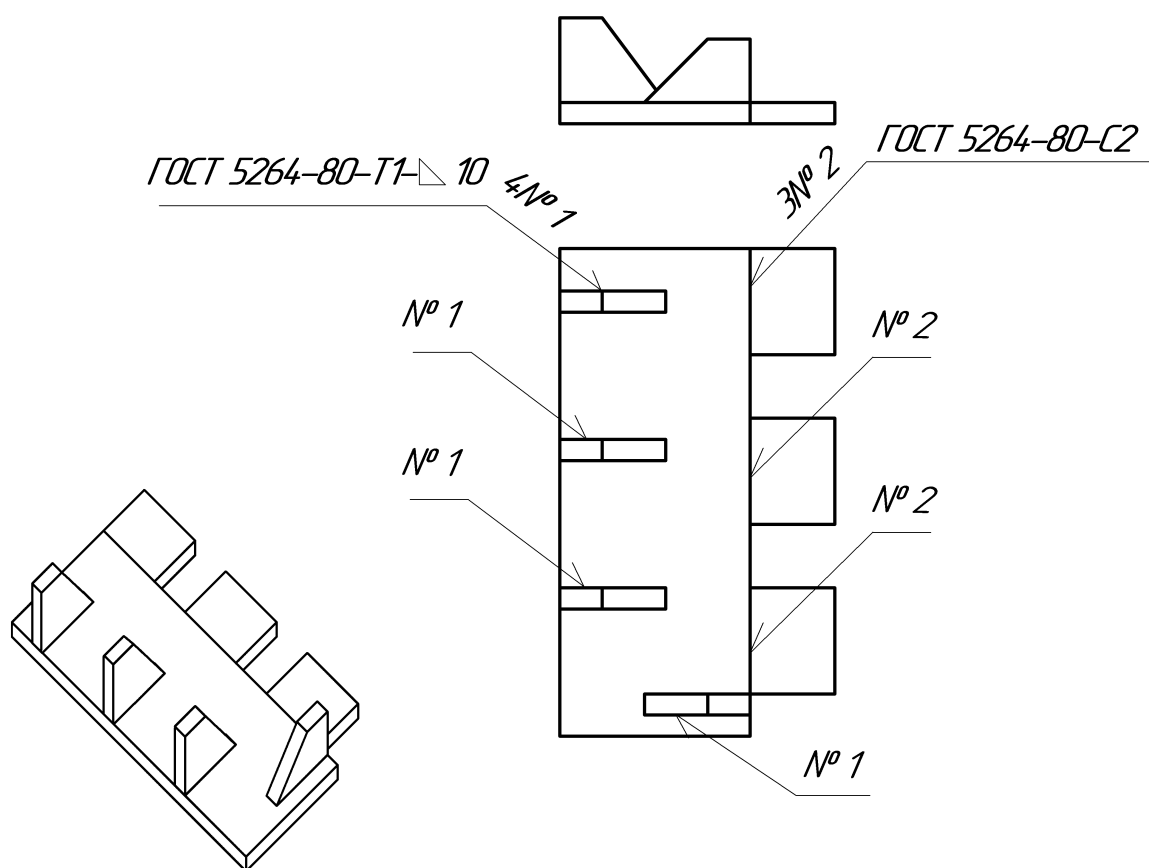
Обозначение на чертежах одинаковых сварных швов
